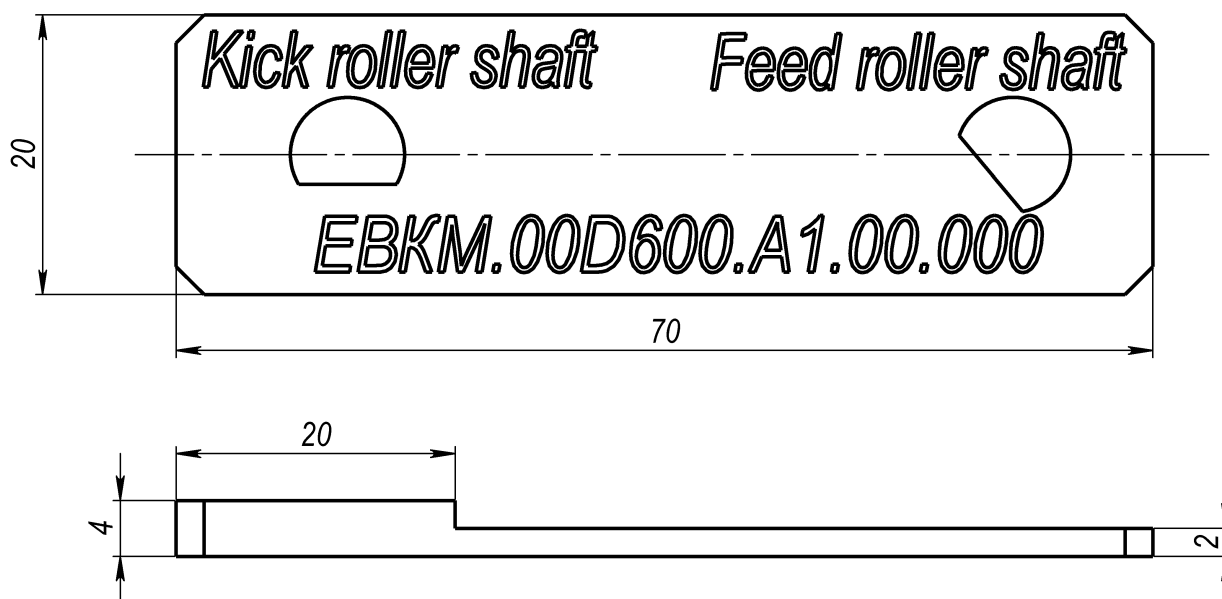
Приспособление для установки фаз роликов EBKM.00D600.A1.00.000
